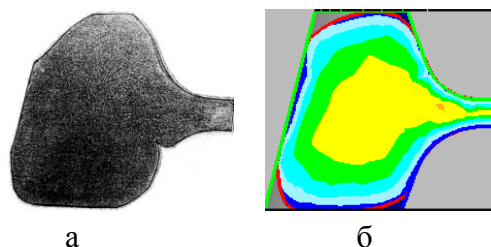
Формоизменение металла в периферийной полости штампов при штамповке заготовок колес Ø957 мм по существующей технологии: а – макроструктура поперечного сечения ободной части заготовки [15]; б – форма поперечного сечения ободной части заготовки, полученная при моделировании (рис. 6б).
